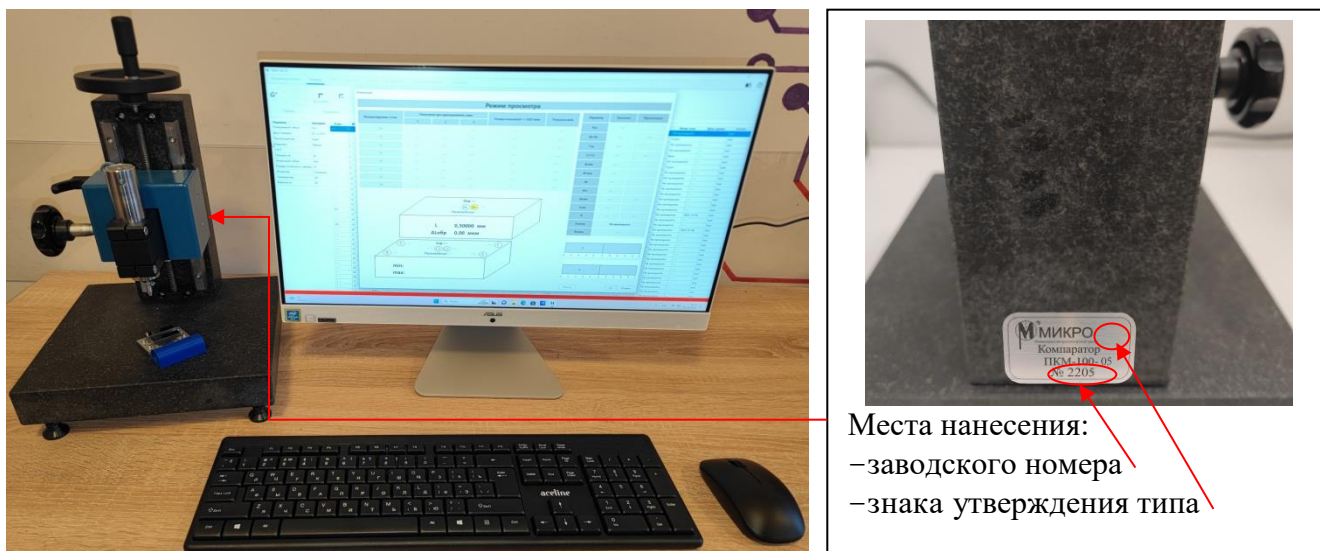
Общий вид компаратора ПКМ-100-05,
